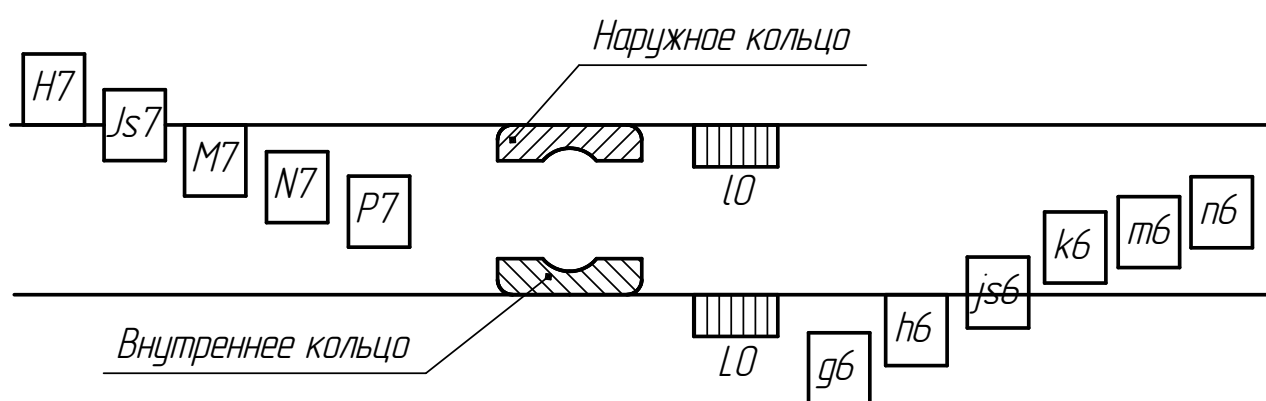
Схема расположения полей допусков при посадках подшипников на валы и в отверстия корпусов
